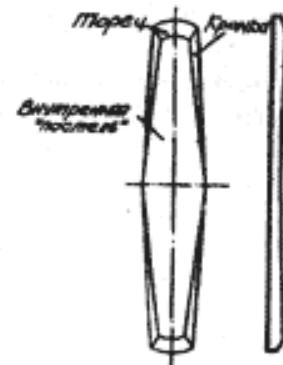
Общий схематический вид готовой клепки-боковика со скошенными кромками
